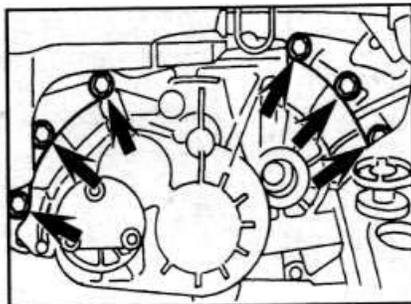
А.29. Расположение 6 болтов крепления левой подвески силового агрегата к коробке передач.
